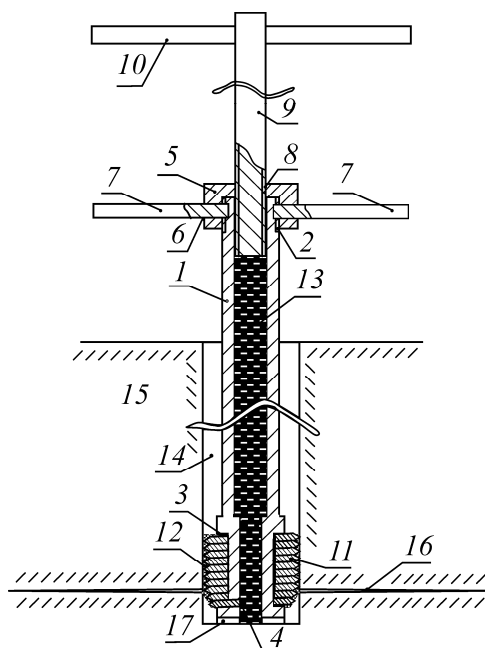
Устройство для разрыва горных пород пластичным веществом поперек скважины: 1 — корпус; 2 — резьба; 3 — кольцевое углубление; 4 — радиальное отверстие; 5 — стакан; 6 — радиальное отверстие; 7 — рукоятка; 8 — центральное отверстие с резьбой; 9 — винт; 10 — рукоятка; 11 — пружина; 12 — герметизирующее вещество; 13 — пластичный флюид; 14 — скважина; 15 — породный массив; 16 — трещина; 17 — радиальные прорезы
